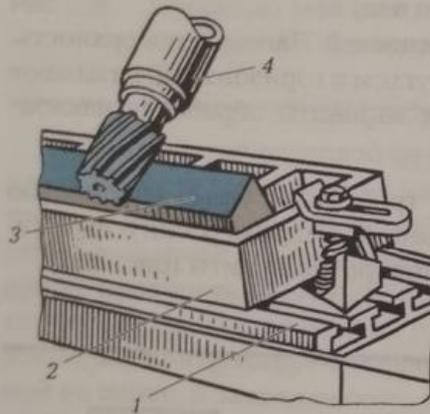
Фрезерование наклонных поверхностей с помощью накладной вертикальной головки:
